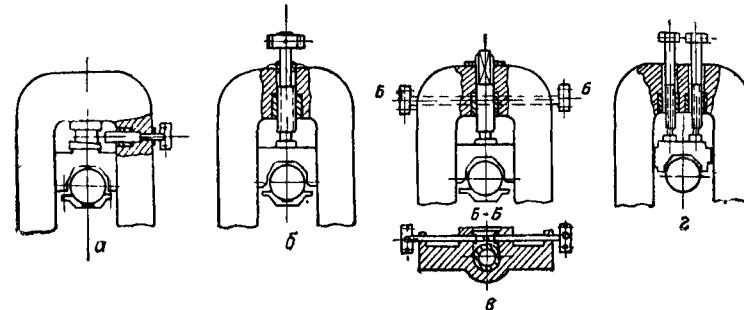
Схемы установочных механизмов верхнего вала с ручным приводом:
